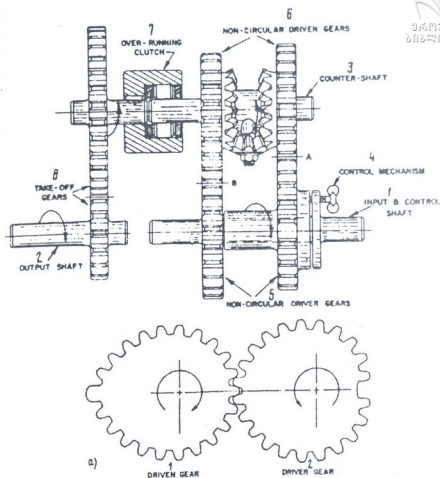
Схема бесступенчатой передачи с некруглыми колесами
